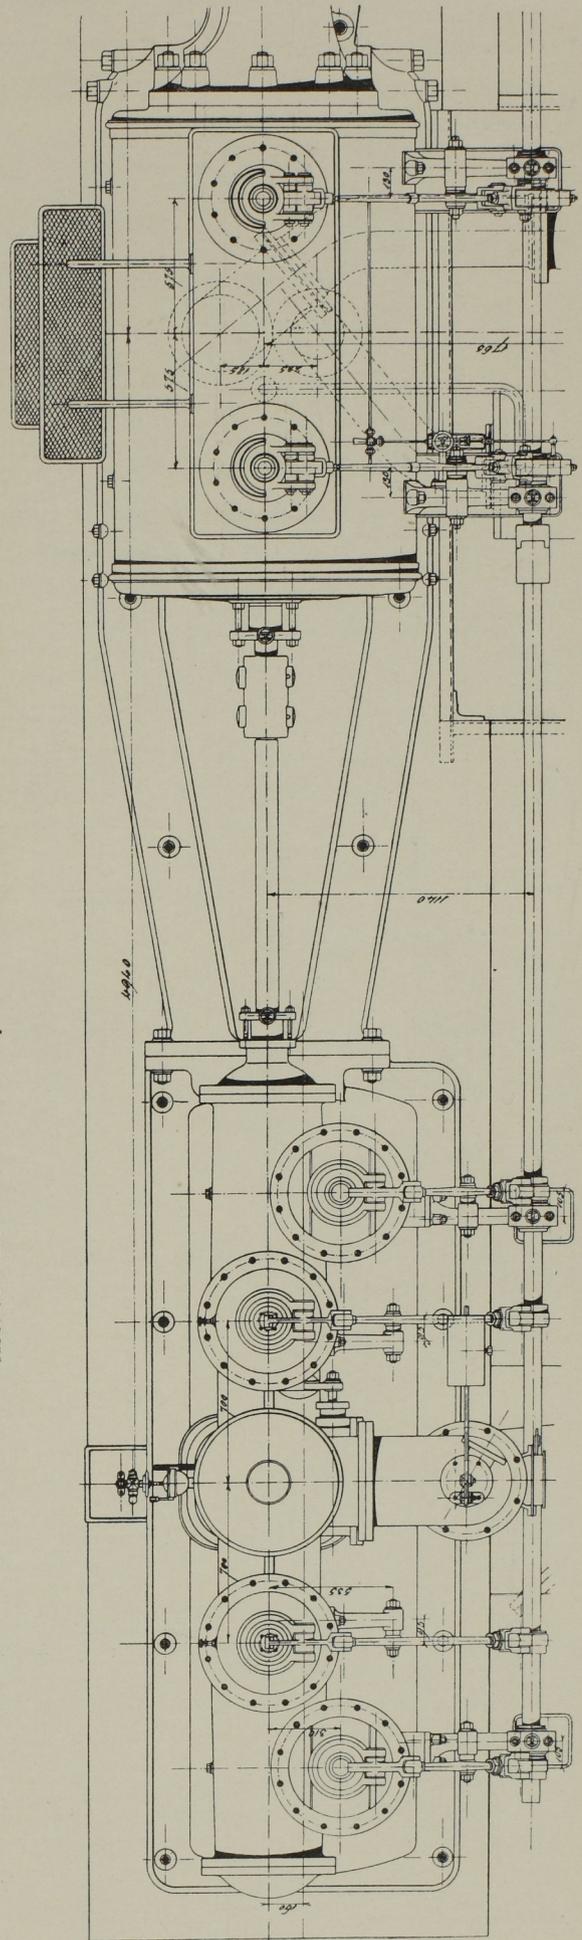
Grundriss der Pumpmaschine. Massst. 1 : 30.
